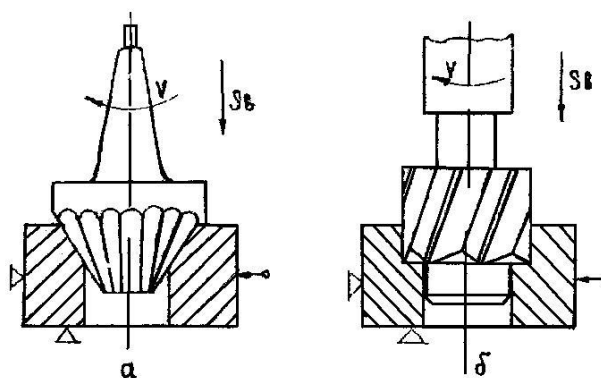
Схеми різання конічним /а/ та циліндричним /б/ зенкером.
